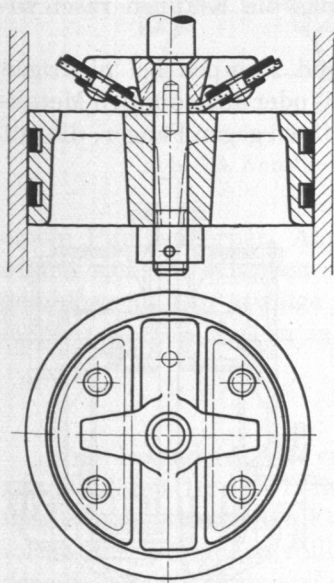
Brunnenpumpenkolben mit Lederklappen.
